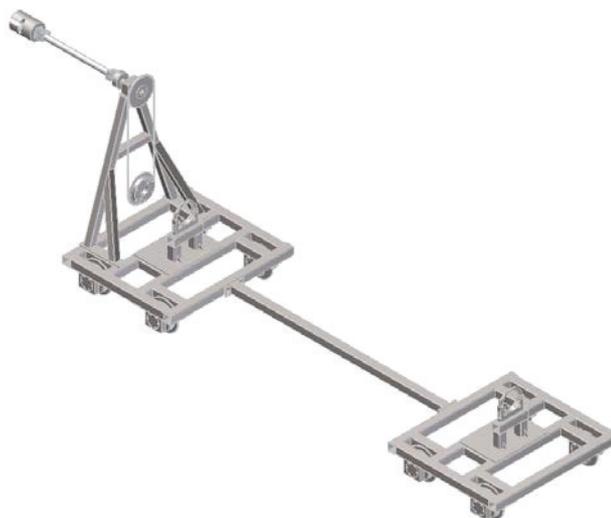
Тележки с приспособлением для вращения оправки в печи
